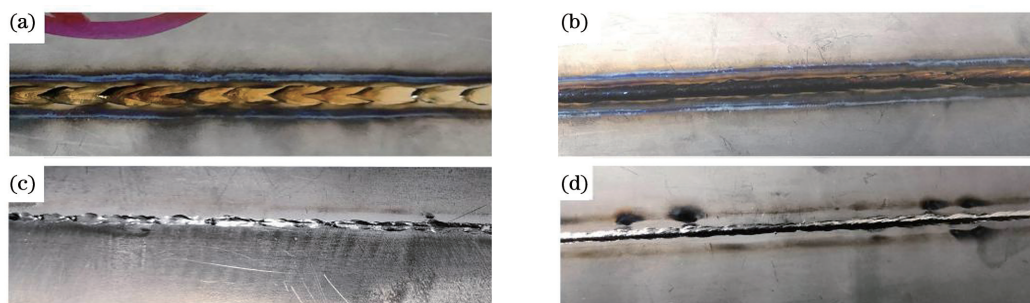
不同焊接速度下焊缝宏观形貌。(a)1.5 m/min, 焊缝正面;(b)1.5 m/min, 焊缝背面;(c)1.2 m/min, 焊缝正面;(d)1.2 m/min, 焊缝背面
